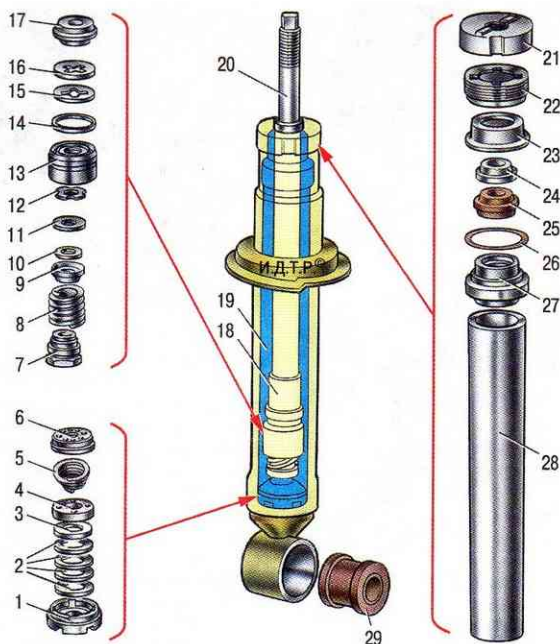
Детали амортизатора задней подвески: 1 – корпус клапана сжатия; 2 – диски клапана сжатия; 3 – дроссельный диск клапана сжатия; 4 – тарелка клапана сжатия; 5 – пружина впускного клапана; 6 – обойма клапана сжатия; 7 – гайка клапана отдачи; 8 – пружина клапана отдачи; 9 – тарелка клапана отдачи; 10 – шайба; 11 – диск клапана отдачи; 12 – дроссельный диск клапана отдачи; 13 – поршень; 14 – кольцо поршня; 15 – тарелка перепускного клапана; 16 – пружина перепускного клапана; 17 – ограничительная тарелка; 18 – дистанционная втулка; 19 – резервуар; 20 – шток; 21 – опора буфера сжатия; 22 – гайка; 23 – обойма сальника; 24 – защитное кольцо штока; 25 – сальник; 26 – уплотнительное кольцо резервуара; 27 – направляющая втулка штока; 28 – цилиндр; 29 – резинометаллический шарнир
